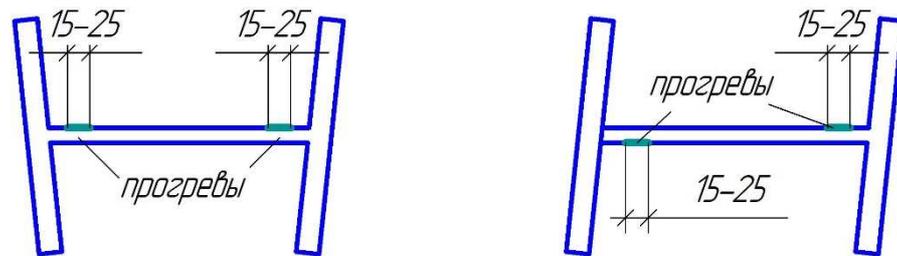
Дефекты перекоса полок на сварных балках
